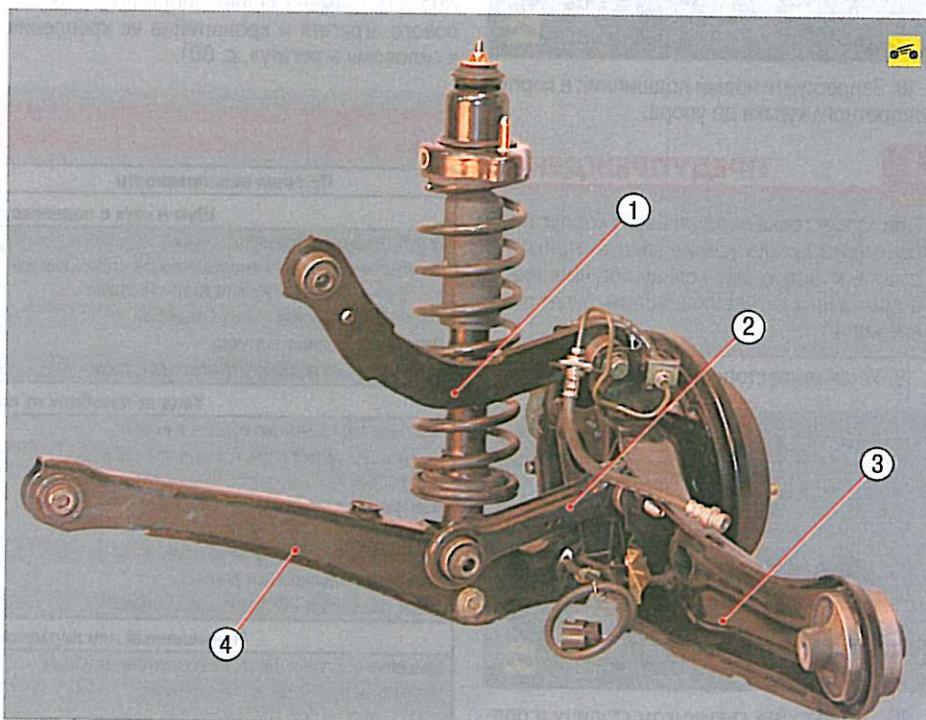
Рычаги задней подвески: 1 – верхний поперечный рычаг; 2 – рычаг управления; 3 – продольный рычаг; 4 – нижний поперечный рычаг
